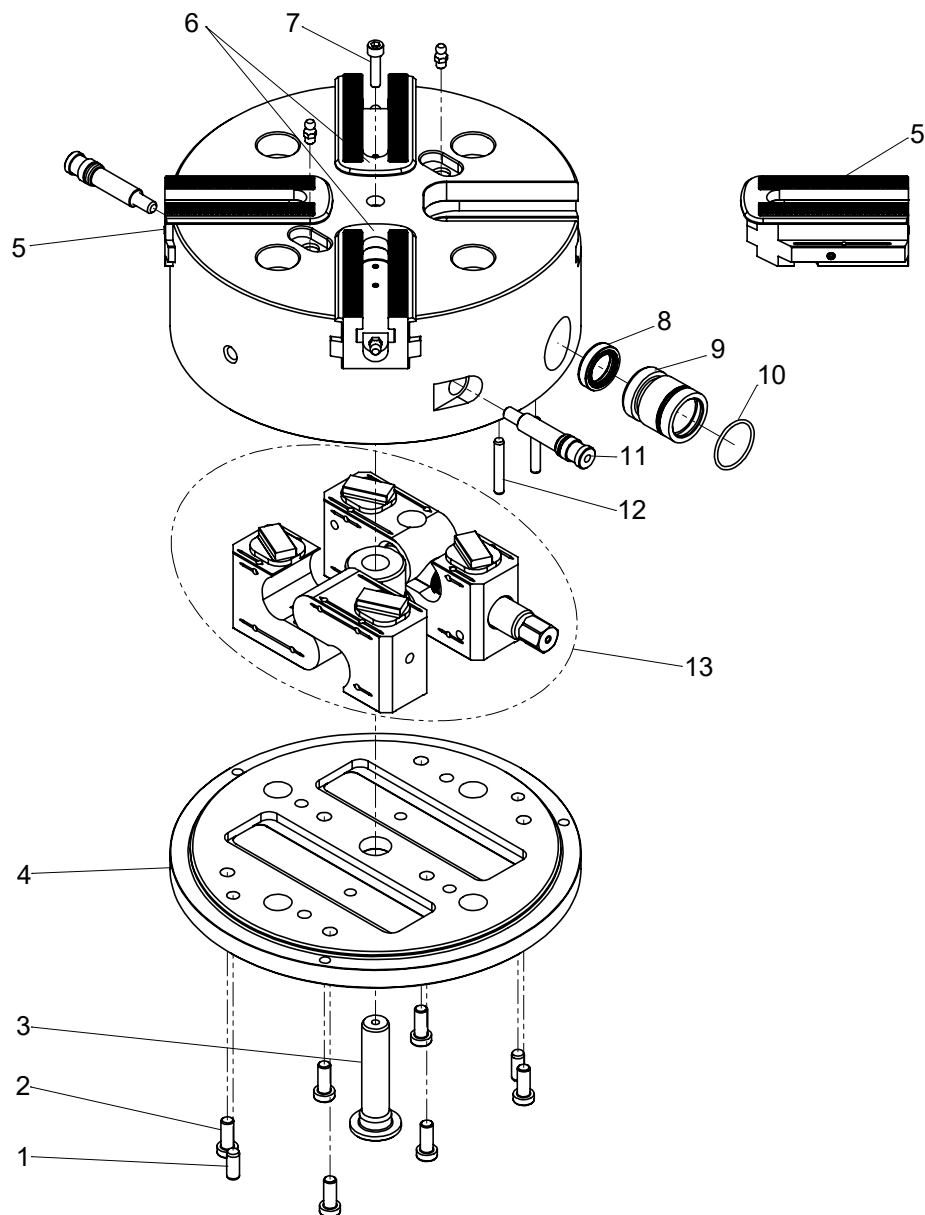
Desmontaje/montaje del mandril de sujeción (VD016 - VD040)
